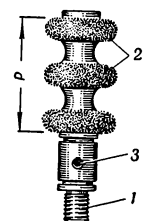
Металлическая щетка (ерш) для чистки канала ствола дробового ружья от ржавчины и удаления свинцовки:
